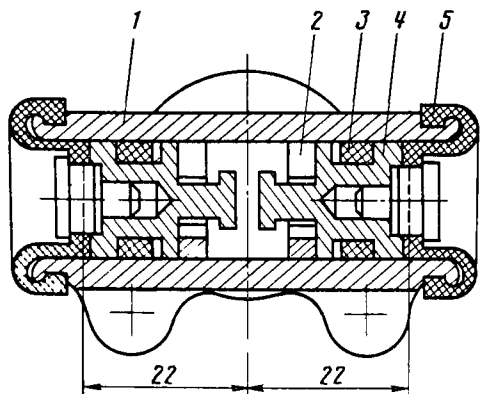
Колесный цилиндр заднего тормоза в сборе: 1 — цилиндр; 2 — упорное кольцо; 3 — манжета; 4 — поршень; 5 — колпак
